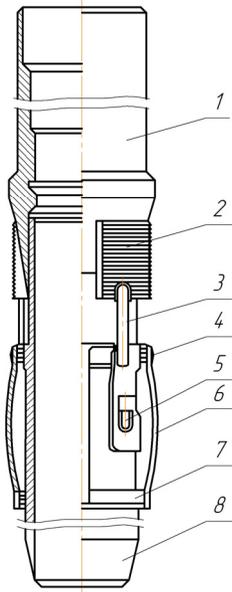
Механическая клиновая подвеска в транспортном положении: 1 – конусообразная муфта; 2 – клиновые плашки; 3 – соединительная пластина; 4, 7 – верхнее и нижнее кольца центратора; 5 – штифт; 6 – пружинный центратор; 8 – корпус
